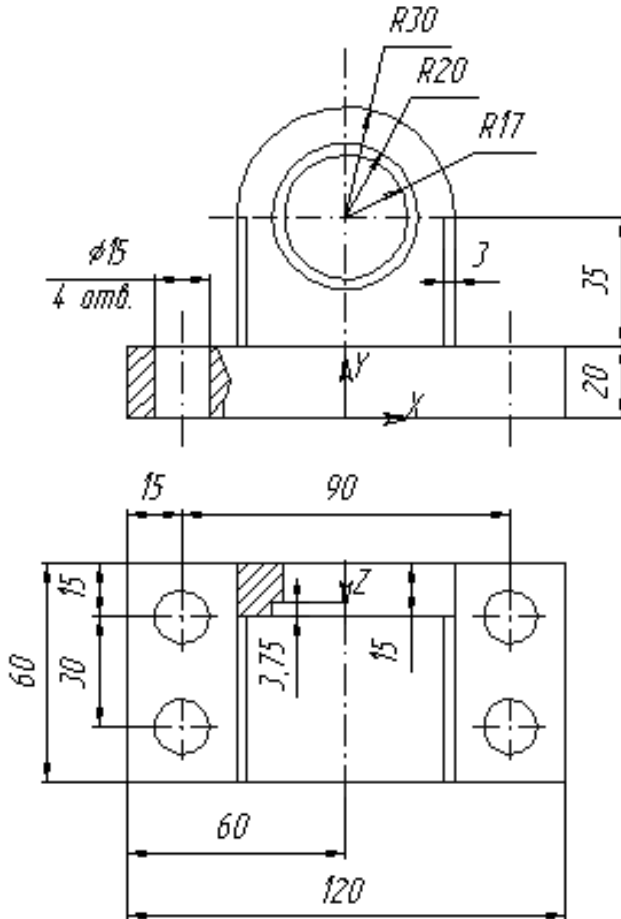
Ескіз опори вала з геометричними розмірами
